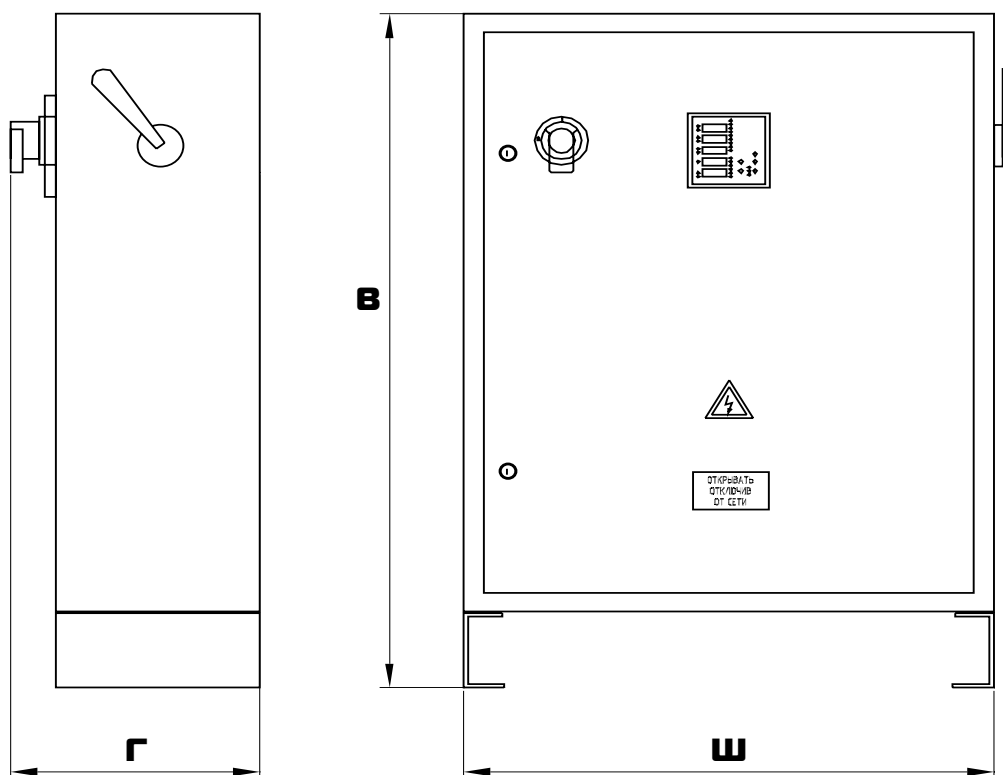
Габаритный чертеж трехфазного ШК-0,4-2
